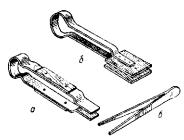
Типы щипцов: а —металлические; б — с деревянными или графитовыми пластинками; в —пинцет.
